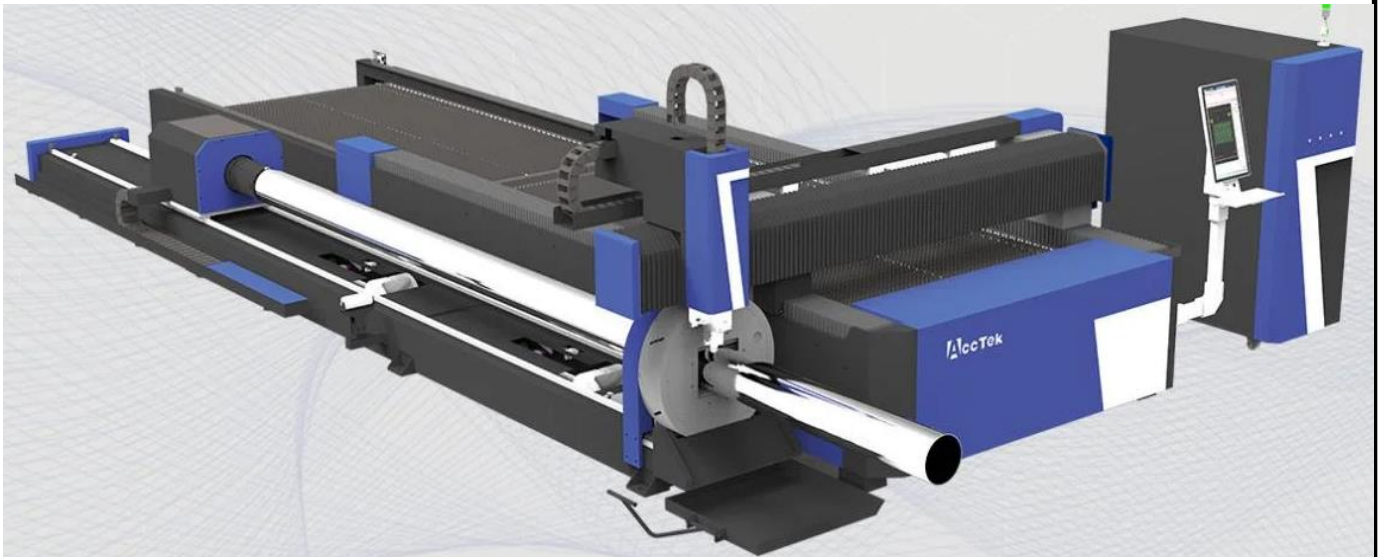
зображення верстату AccTek Fiber laser cutting machine With 2nd Table & Rotary axis
